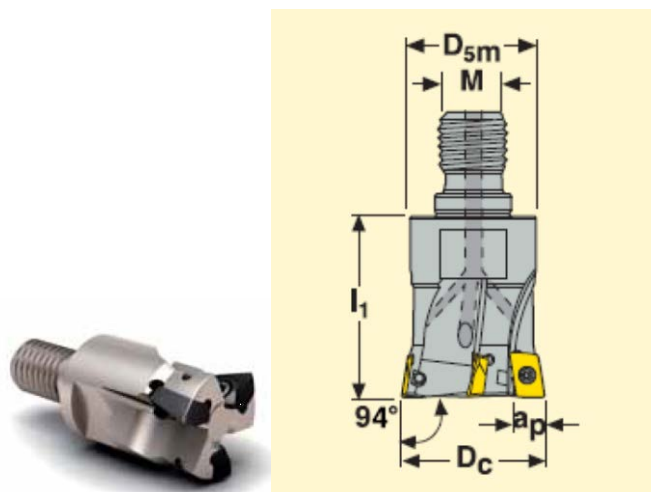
Фреза для врезного фрезерования R217.79–144RE-09-5AN
